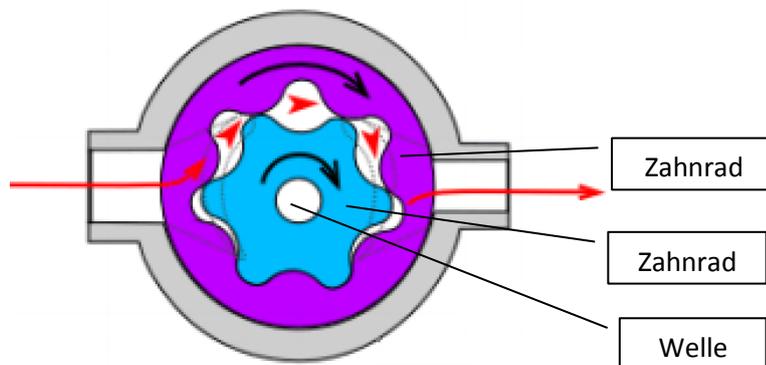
Aufbau einer Zahnringpumpe [Winkler2016, S.18]
